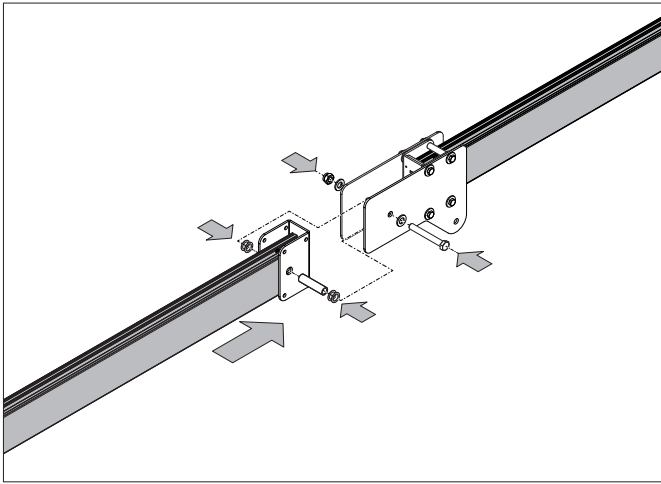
MONTAGGIO MEMBRO / ROD ASSEMBLY
